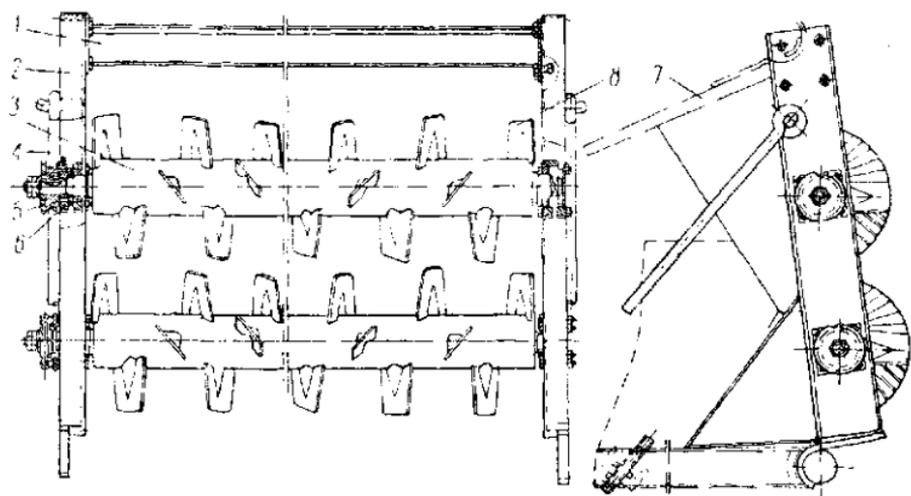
Разбрасывающее приспособление РПТУ-2,0:
